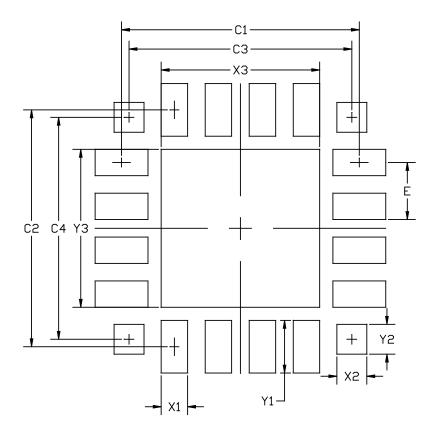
QFN20 PCB 焊盘布局图
